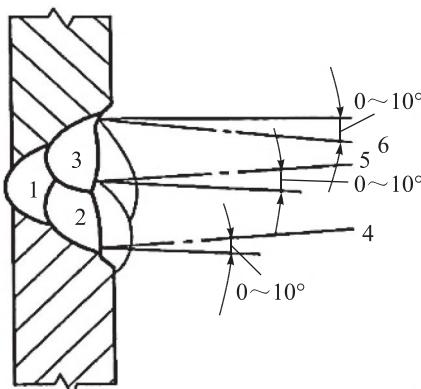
盖面层焊接焊枪的角度（板对接横焊）
